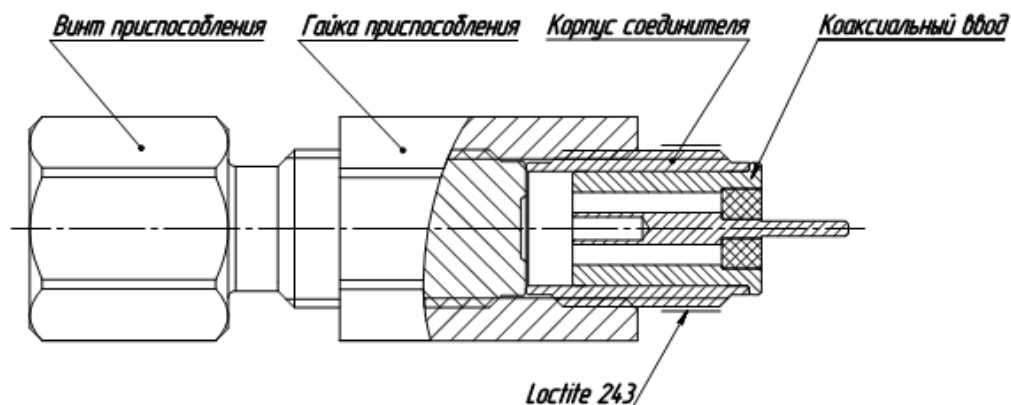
Установка коаксиального ввода в корпус соединителя
